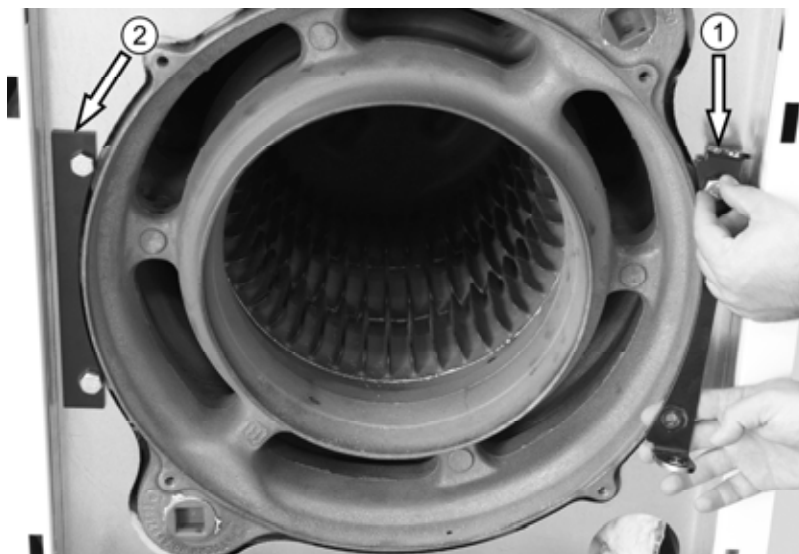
La plaque charnière ① est en principe préinstallée à droite. En cas de besoin, la plaque charnière ① peut être montée à gauche ② et la plaque de retenue respectivement à droite.
